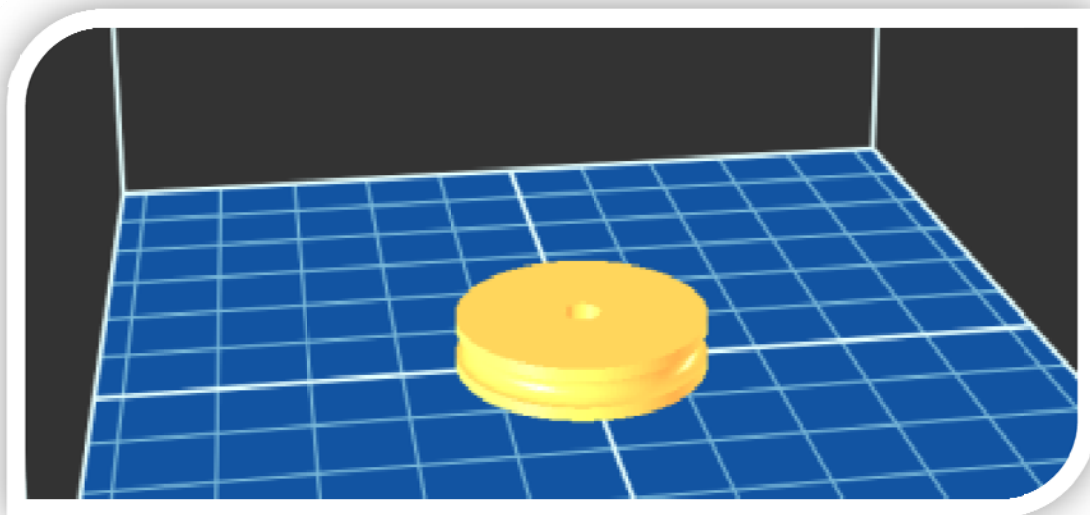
Posición de impresión de la rueda loca. [Fuente: Elaboración propia.]
